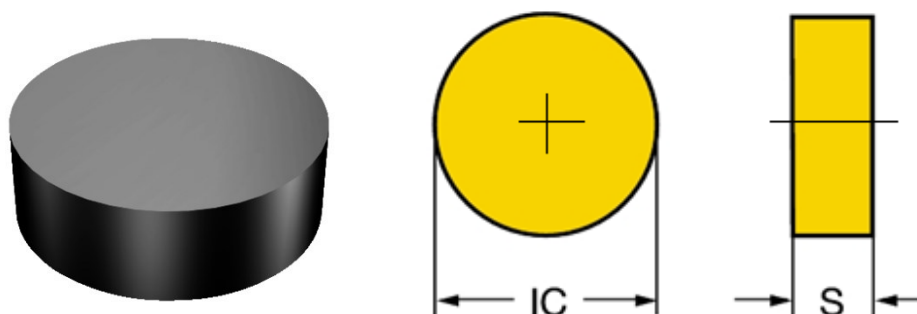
Tvar a geometrie RNGN 120700 T0120 6060 [41]
